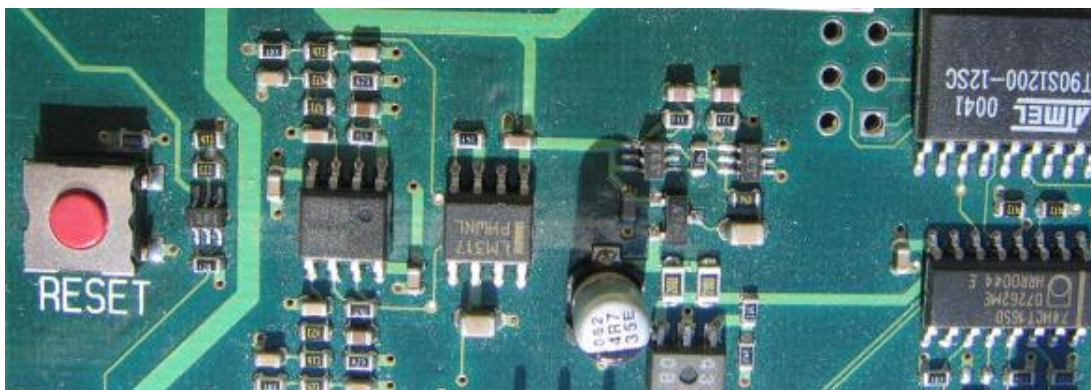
Exemplos de conexão SMD e Componentes SMC
